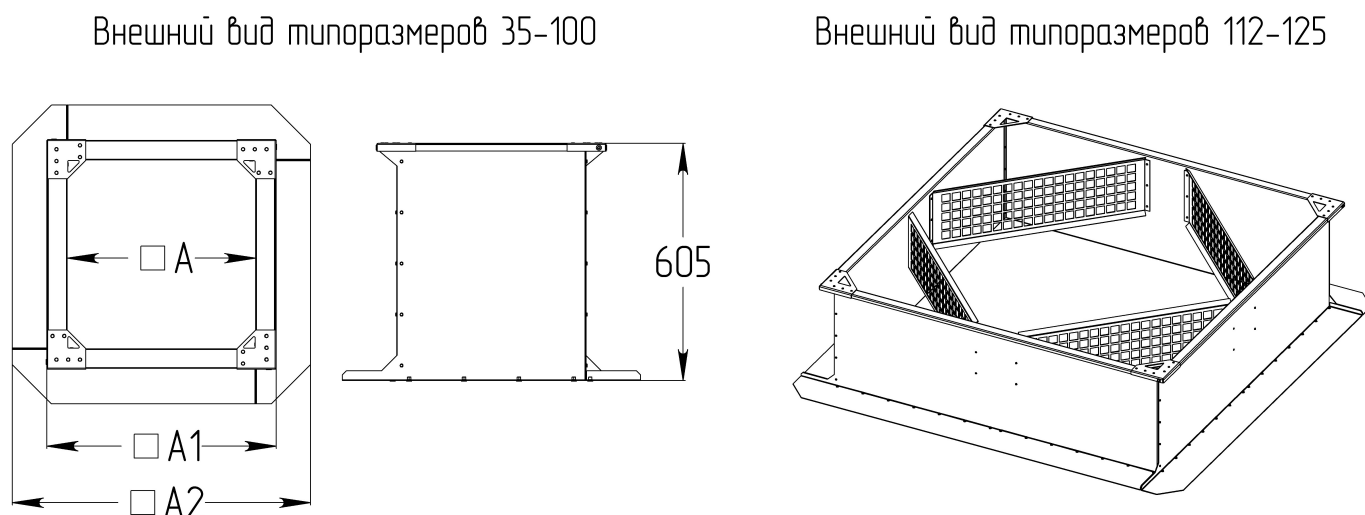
Внешний вид и основные размеры монтажного стакана SMV/SMV-U
